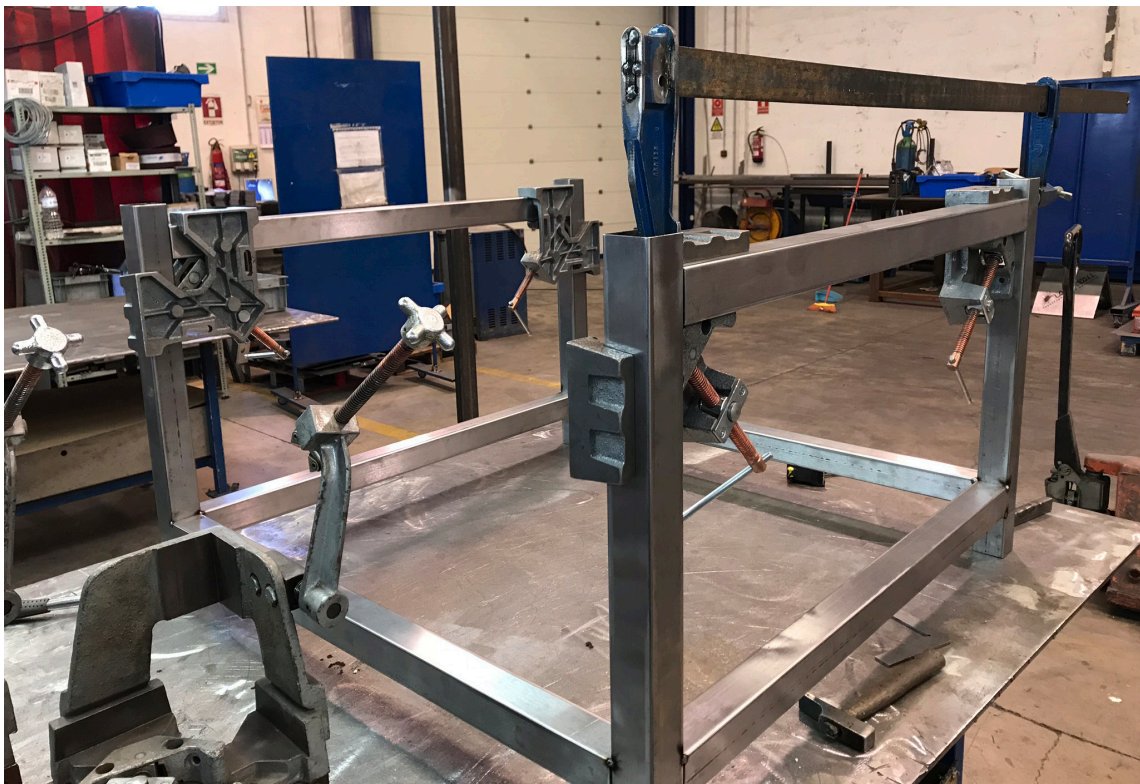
Colocación refuerzos “Estructura 50x50x2”
